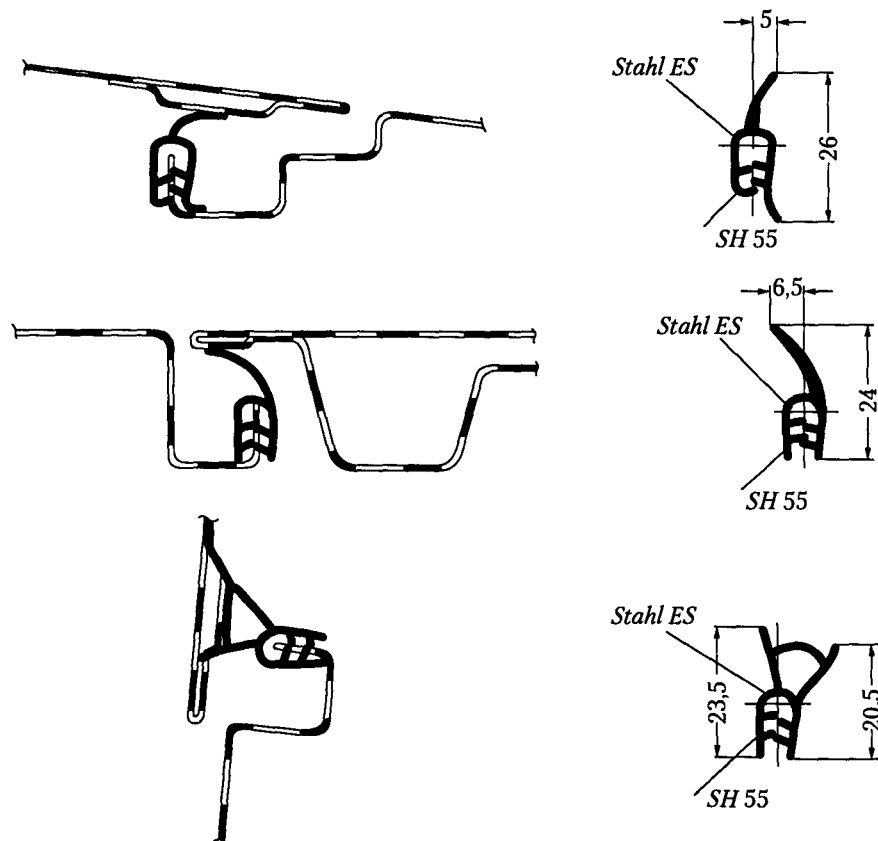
Некоторые виды металлопластмассовых профилей и способы их монтажа на корпусе автомобиля [38]
